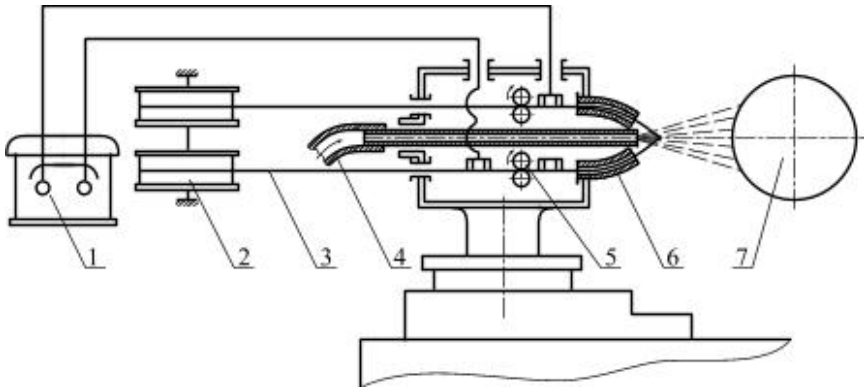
Схема установки для электродугового газотермічного наплення: 1 – джерело живлення; 2 – котушки; 3 – електродний дріт; 4 – трубка для подачі стиснутого інертного газу; 5 – ролики; 6 – напрямні наконечники; 7 – деталь
